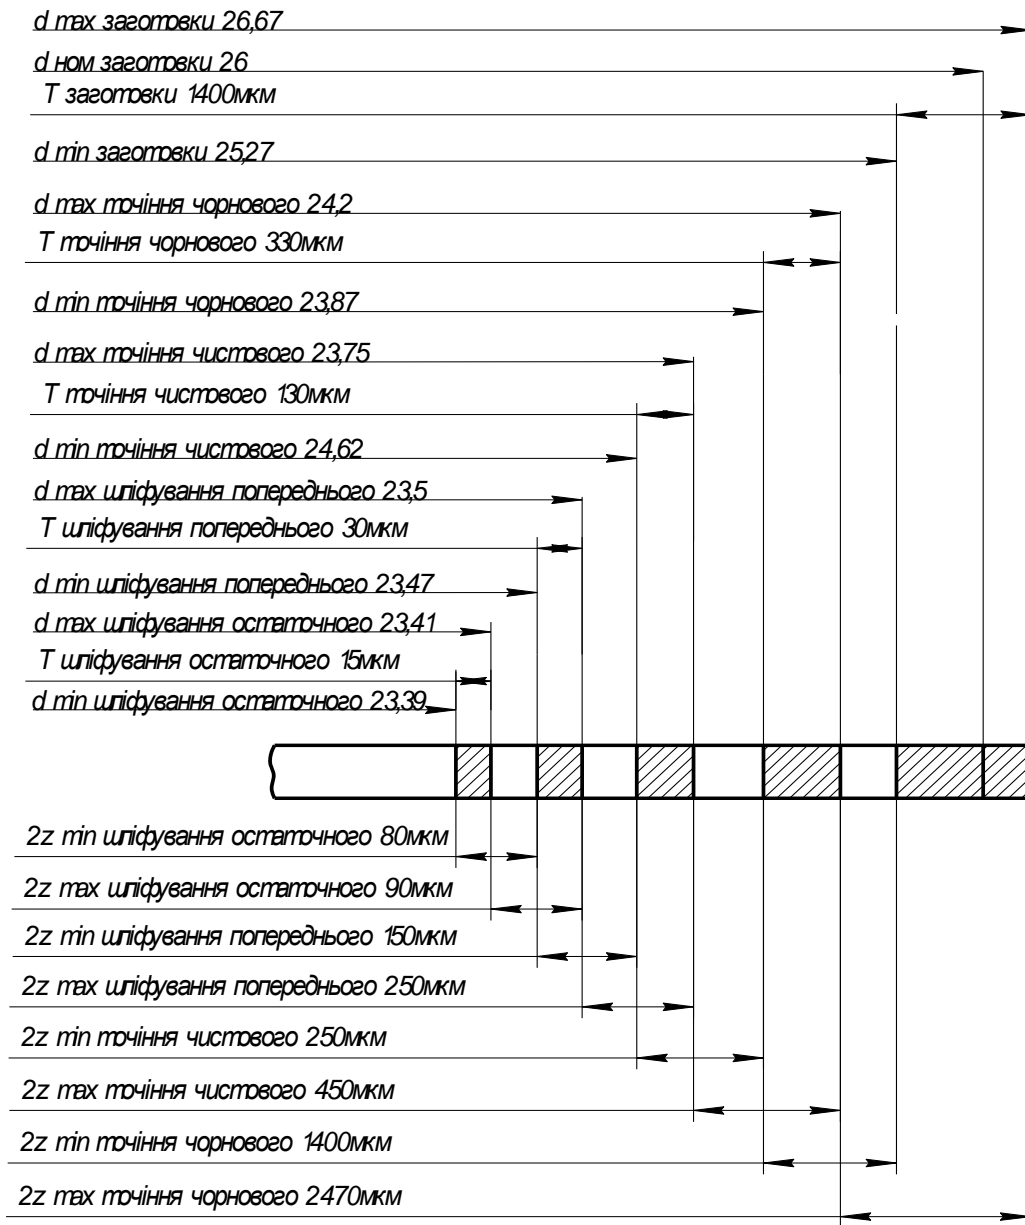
Схема графічного розташування припусків і допусків на обробку поверхні $\varnothing 23, 4f7$
